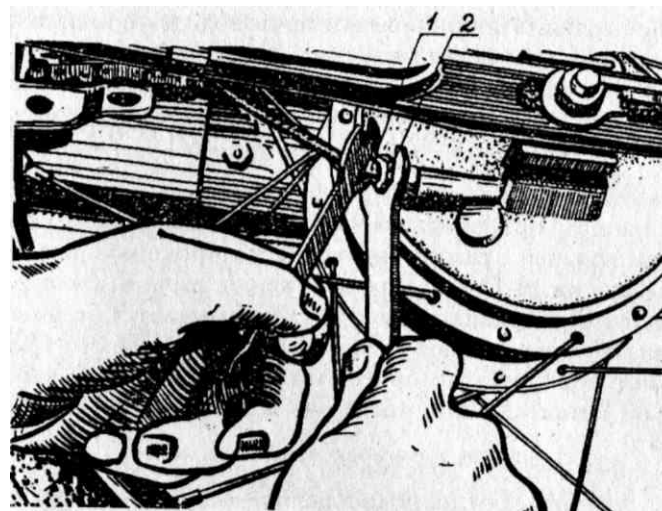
Регулировка тормоза заднего колеса: 1 - упор; 2 - гайка
